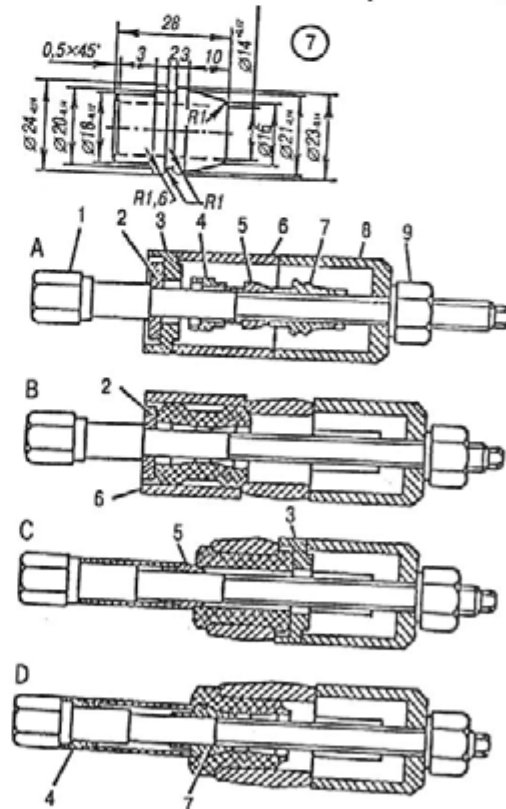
Приспособление 7823-6898 для замены резиновых втулок передней подвески и его применение: 1 - болт; 2 - шайба; 3 - фланец; 4, 5, 7 - оправки; 6 и 8 - корпуса; 9 - гайка; А - приспособление в сборе; В - исходное положение для монтажа резиновой втулки в верхние рычаги; С - исходное положение монтажа распорной втулки в верхние рычаги; D - исходное положение для монтажа распорной втулки в нижние рычаги
